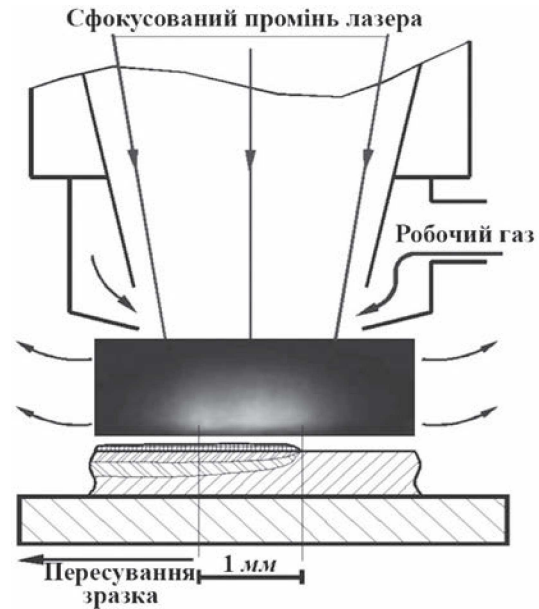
Схема лазерно-плазмової обробки металу із зображенням приповерхневої плазми оптичного пульсуючого розряду
